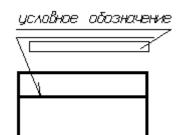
Структура условного обозначения нестандартного шва или одиночной сварной точки
